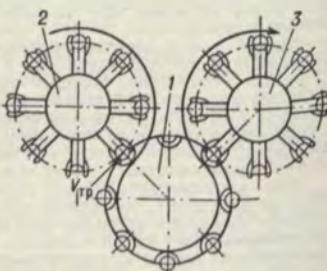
Схема питания рабочего ротора предметами обработки: 1 — рабочий ротор; 2 — питательный транспортный ротор; 3 — приёмный транспортный ротор; V_{tr} — общая транспортная скорость предметов обработки и орудий.
